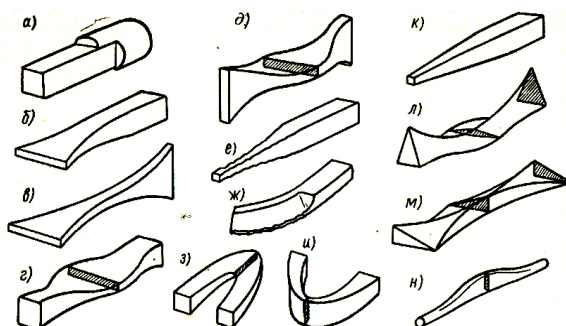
Основные формы заготовок, получаемых методомковки: а – проковка круглой заготовки на квадрат; б – клиновидное уширение штабика; в – заготовка в форме винта; г – заготовка с расплющенной средней частью; д – клинообразные концы с расширенной серединой; е – заготовка с утонением одного конца; ж – получение заготовки треугольного профиля; з – дугообразная разностенная заготовка; и – то же с разной толщиной вершины дуги; к – заготовка с заостренным концом; л – заготовка треугольного профиля с переменными по длине сечениями; м – кованая заготовка сложной формы; н – круглая заготовка, прокованная на плоскость посередине [6]
